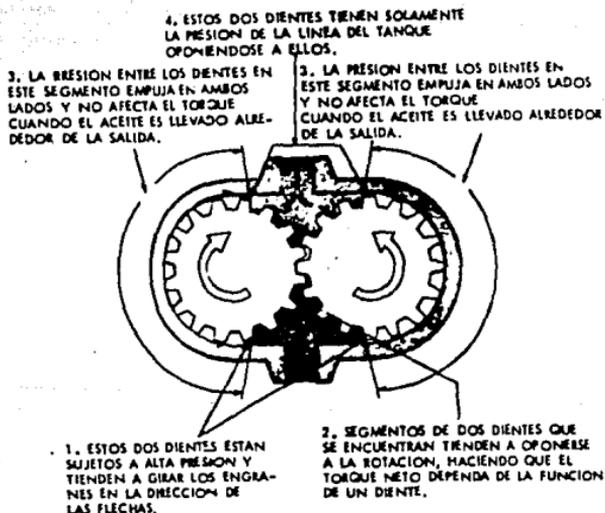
Descripción de el Torque en un Motor de Engranes.
